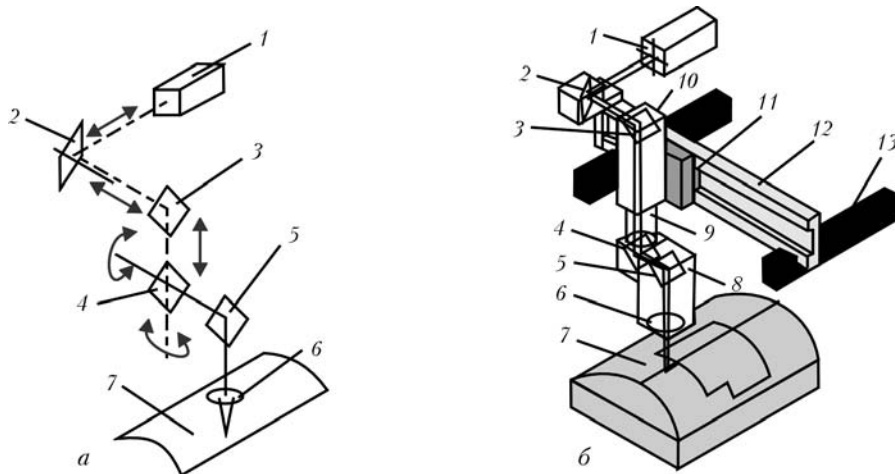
Координатне (а) і конструкційне (б) компонування 5-координатного ЛТО: 1 – випромінювач лазера; 2–5 – дзеркала поворотні; 6 – лінза; 7 – заготовка; 8–12 – блоки рухомі; 13 – напрямні
